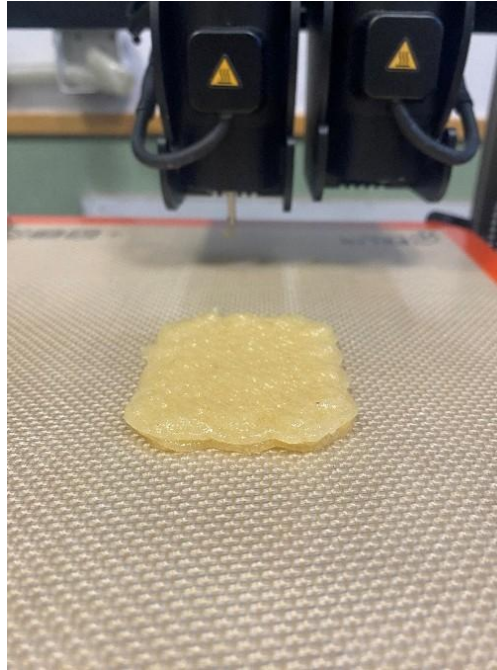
Efecto de la superficie y método de deposición de Ensayo E-X-02
